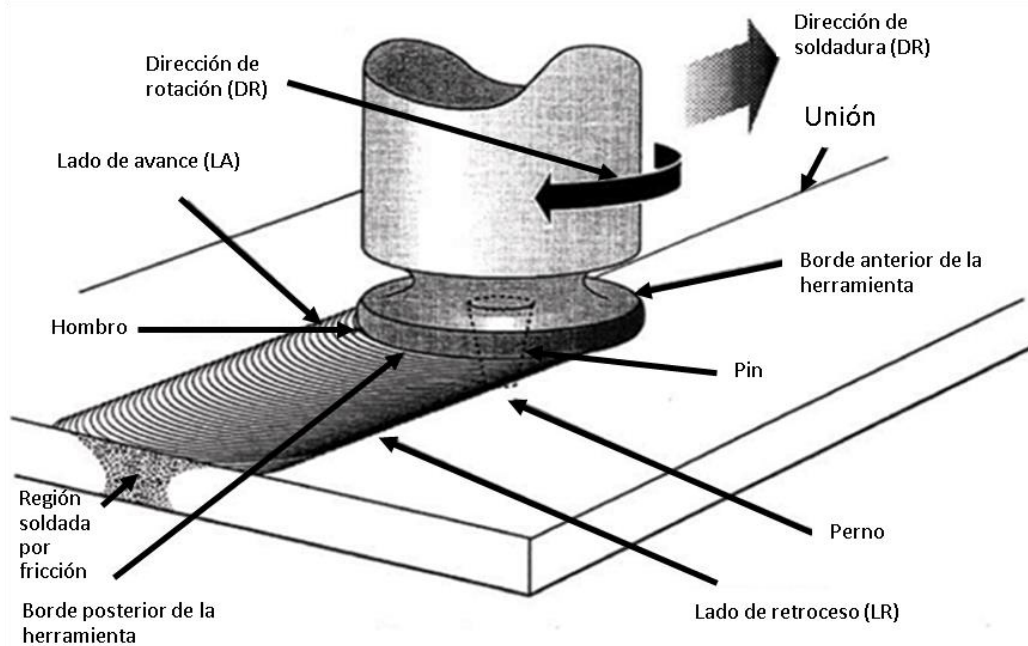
Soldadura por fricción en una configuración de junta a tope.
